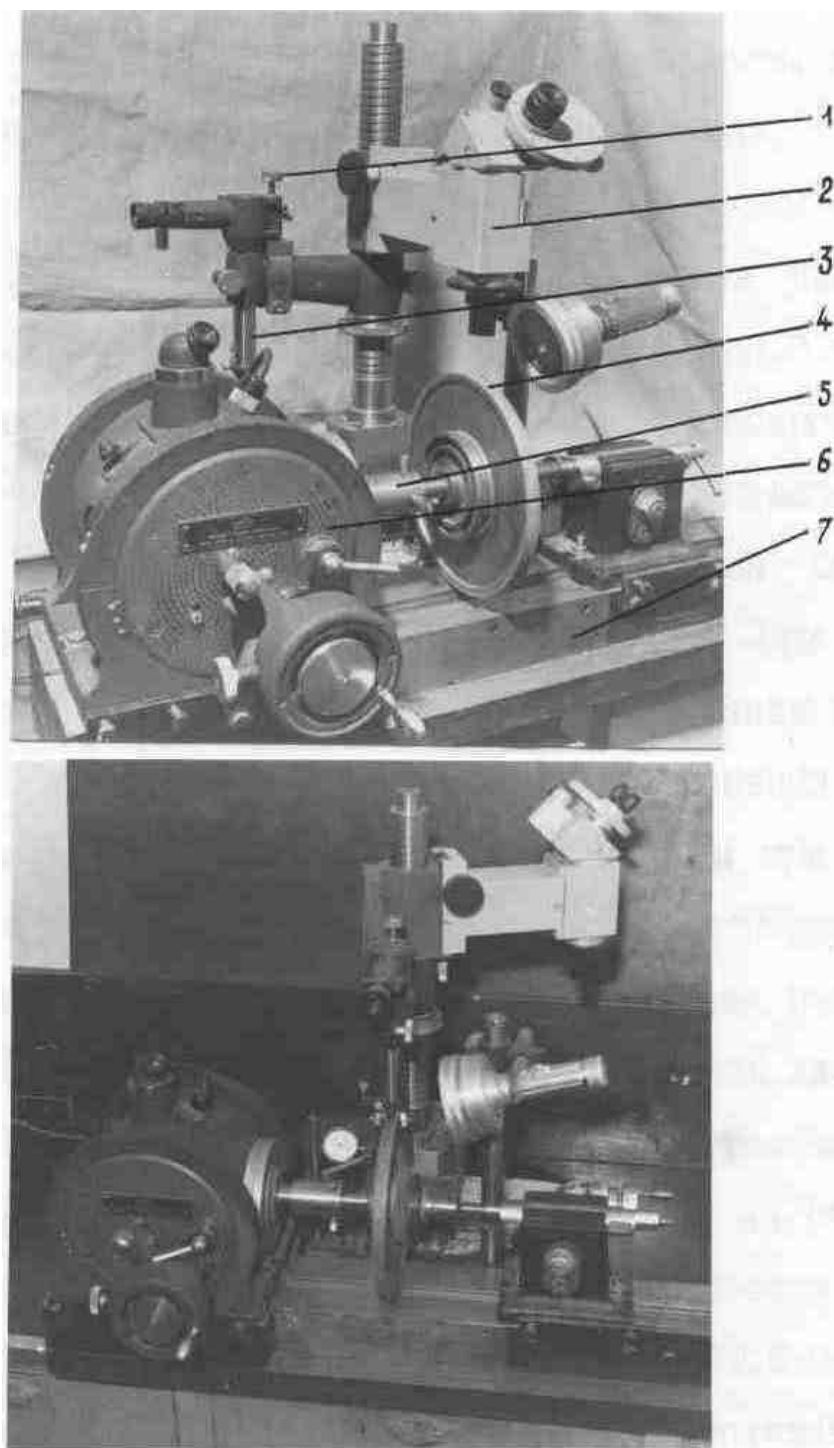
Установка для изучения расположения зерен на рабочей поверхности круга.
